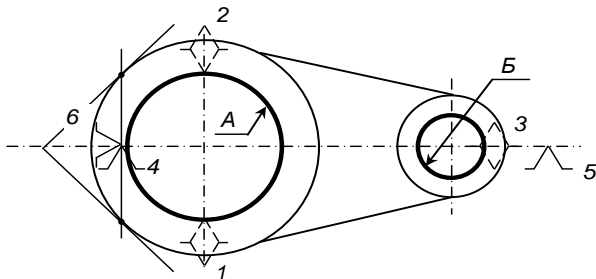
Схема базування заготовки деталі типу «Важіль»
